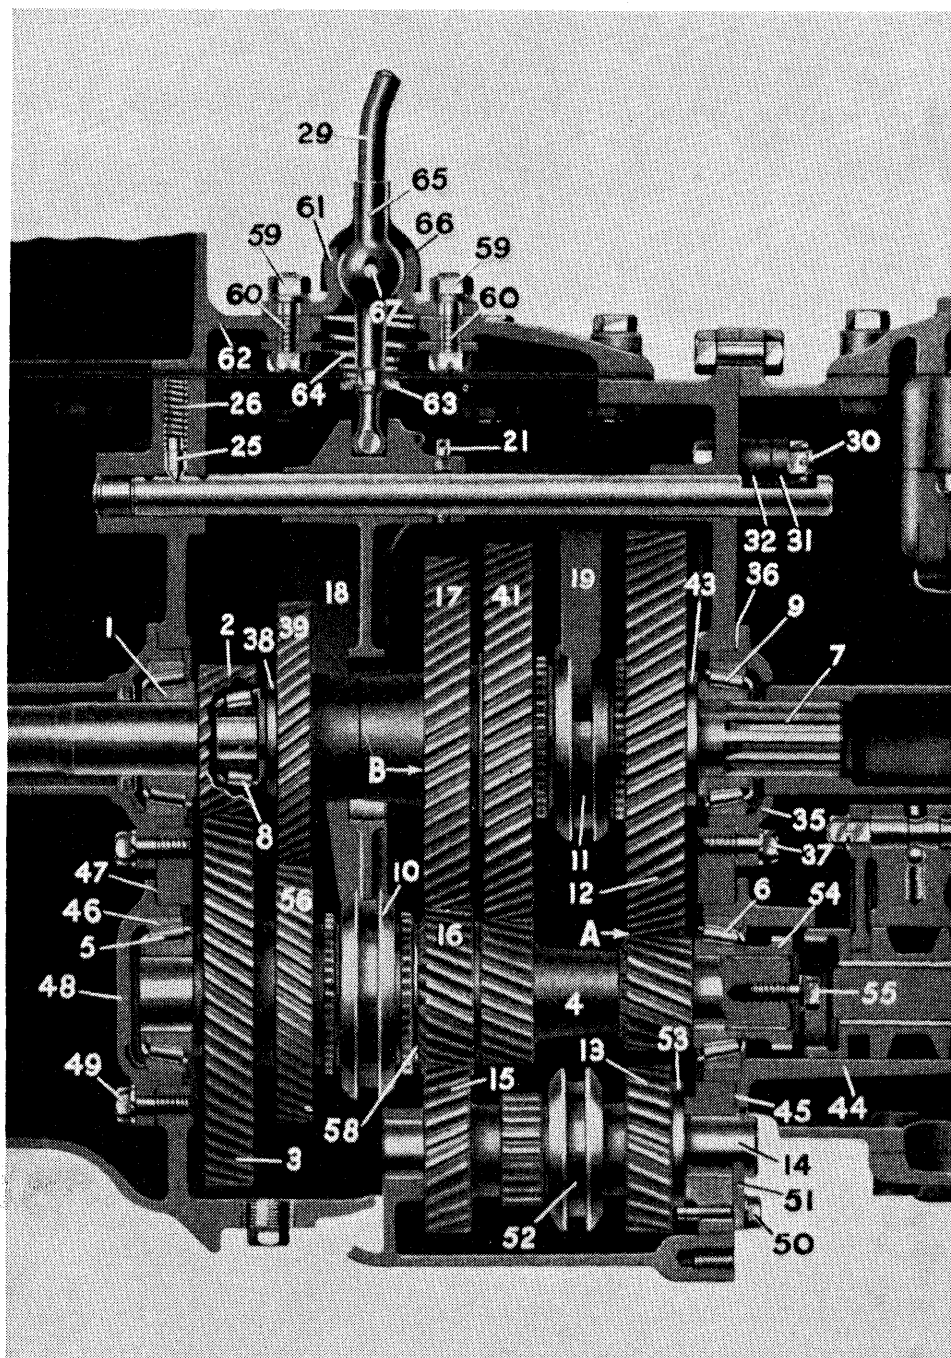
Gearkassens opbygning (se tillige fig. 26 og fig. 27).
